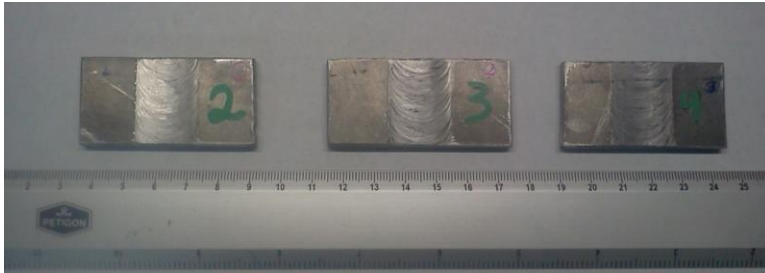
Corte de placas previo a su montaje en baquelita.
